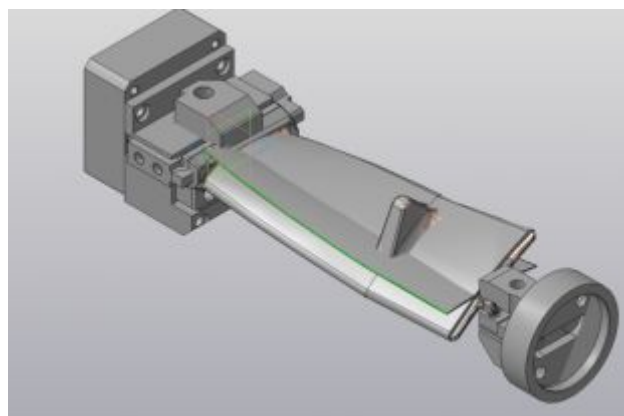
Общий вид приспособления для ленточного шлифования профиля пера лопаток третьей ступени КНД
